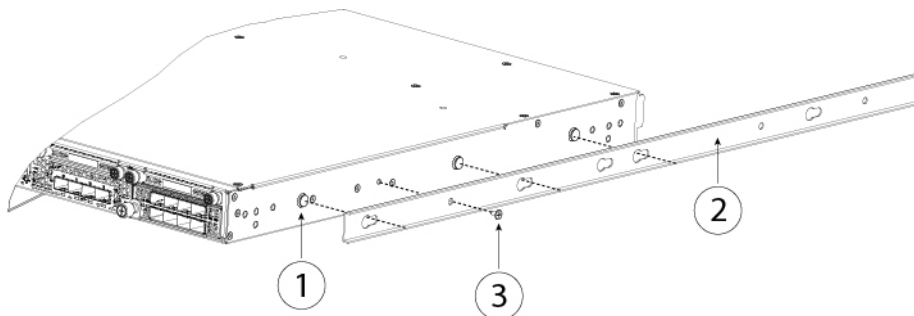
Inserimento delle viti sullo chassis 2110/2120 e allineamento della guida interna
